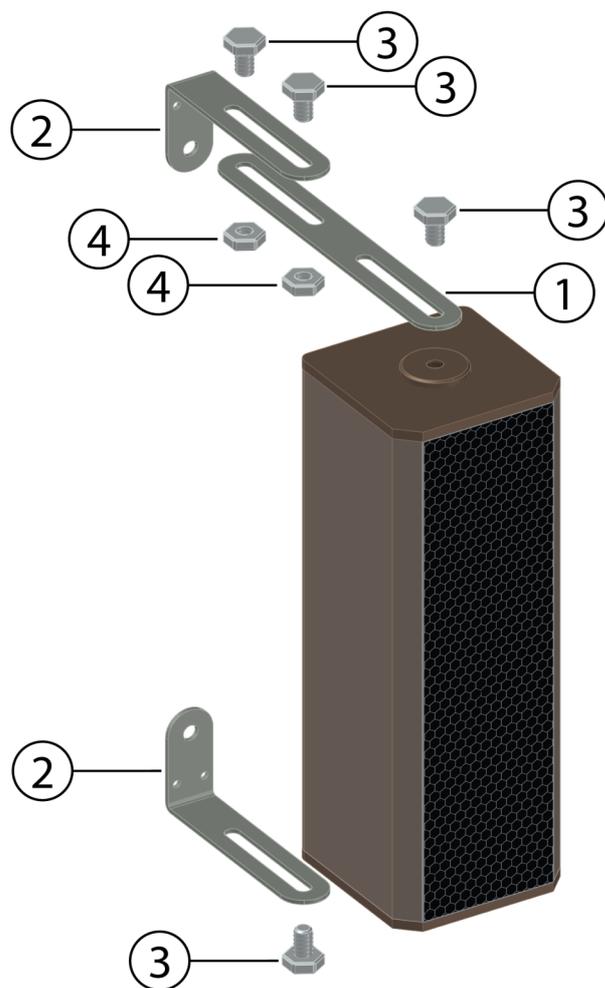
Комплект крепежных принадлежностей и установка крепежа БА
